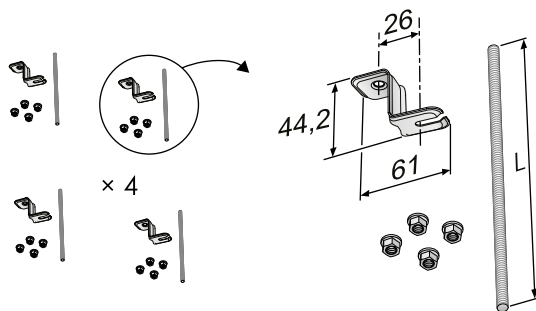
Montageteil SYST MS M8-1, Deckenbefestigung Gewindestange
